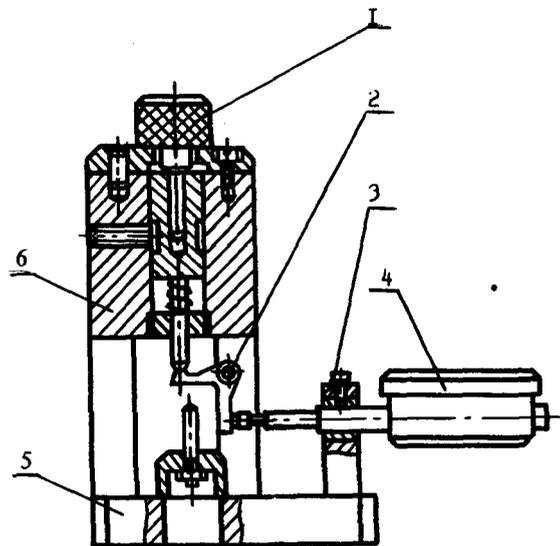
Приспособление для контроля двух линейных размеров деталей типа валиков:
